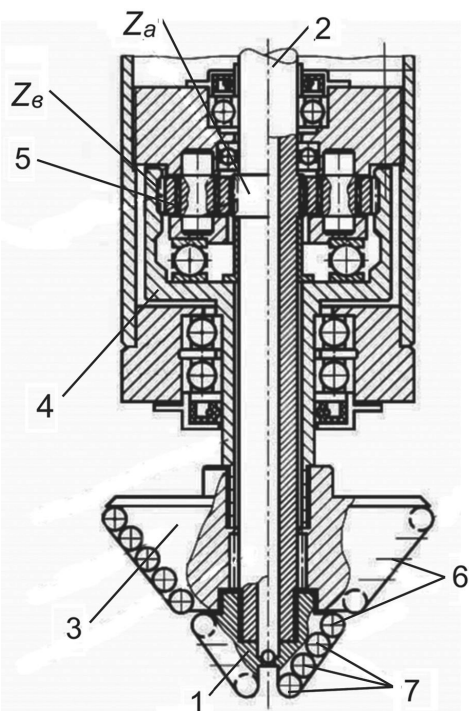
Долото Д-2ВВ с редуктором: 1 — пилотный ярус; 2 — привод от забойного двигателя; 3 — скважинообразующий ярус; 4 — привод от планетарного редуктора; 5 — планетарный редуктор; 6 — режущие лопасти; 7 — режущие элементы; z_a и z_b — количество зубьев на центральном колесе и зубчатом венце планетарного редуктора соответственно
